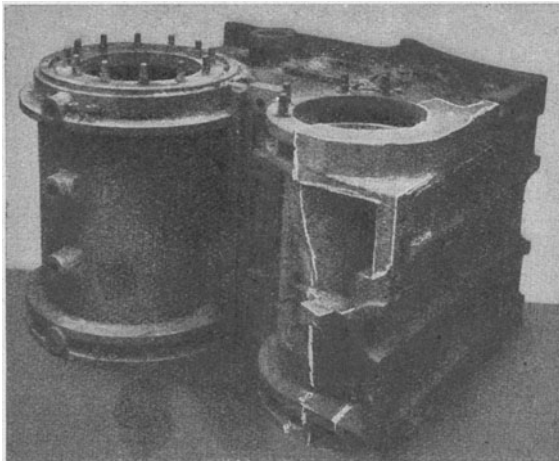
Obiger Lokomotivzylinder elektrisch geschweißt.
